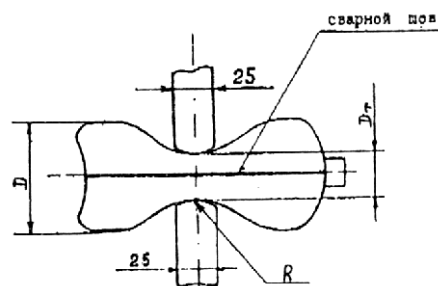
Испытание корпуса огнетушителя на сдавливание:
